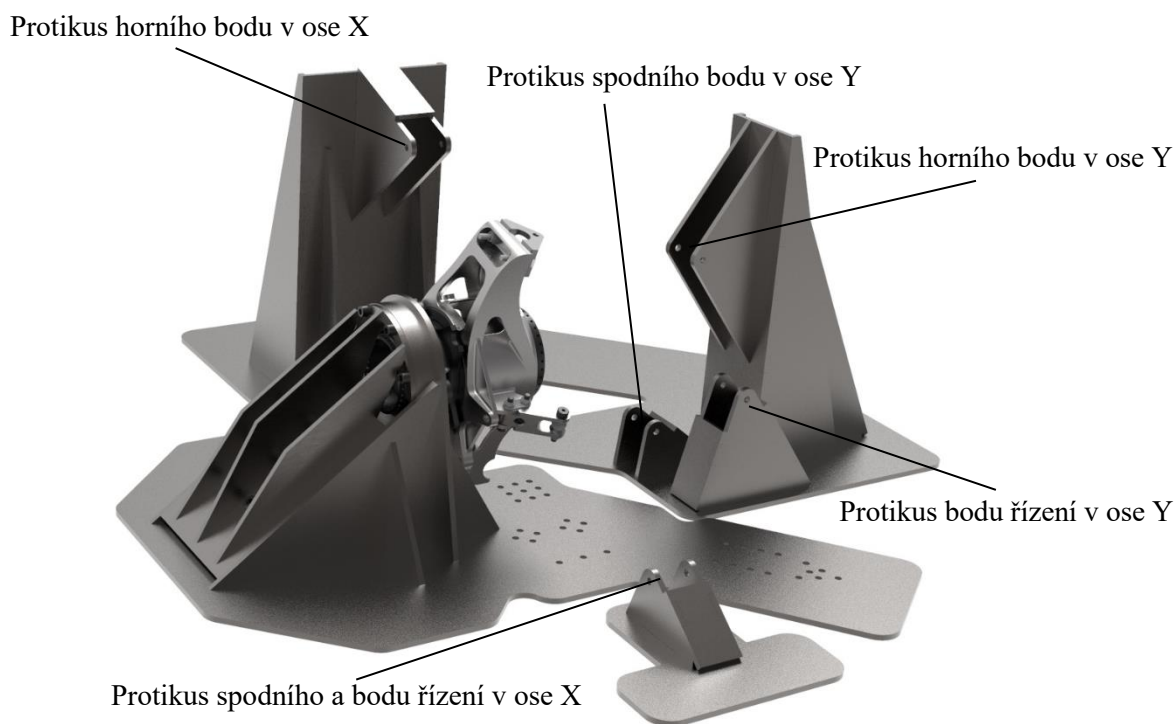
Držáky spodního bodu, horního bodu a bodu řízení
